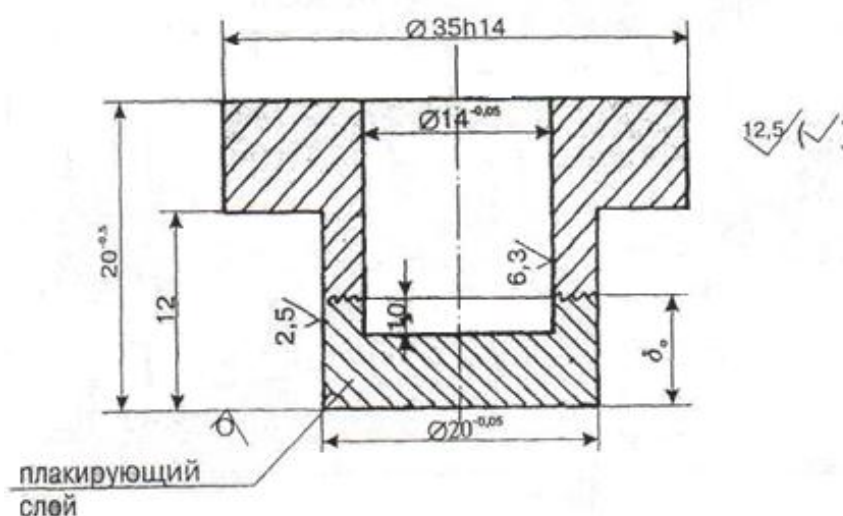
Образец для испытания двухслойной стали на отрыв
